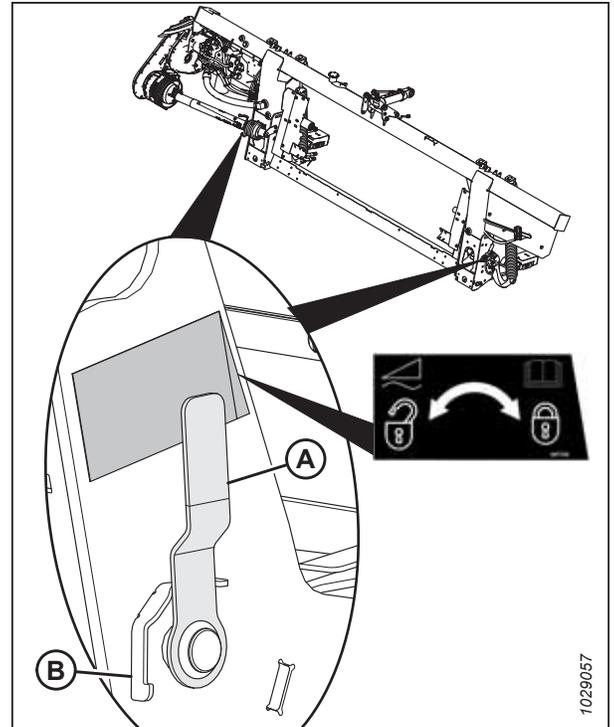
Dispositivo di bloccaggio flottazione della testata in posizione di blocco
